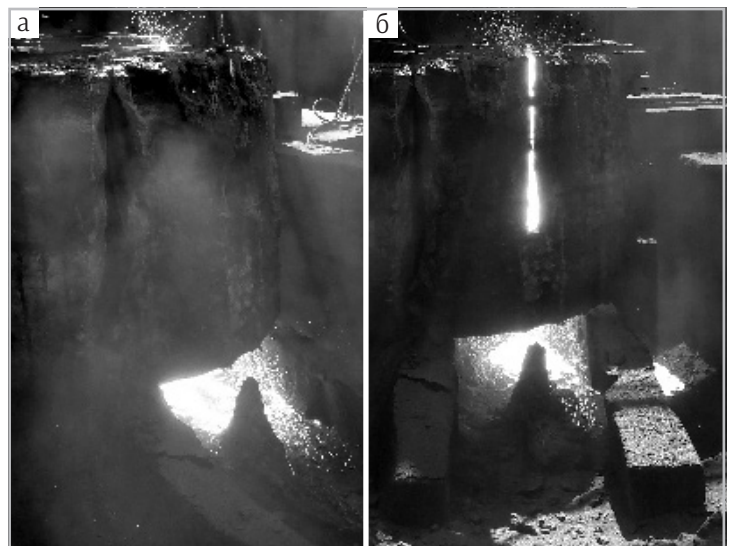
Кислородная резка поковки толщиной 1700 мм из стали 34ХМФ: а — вид сбоку; б — вид спереди
